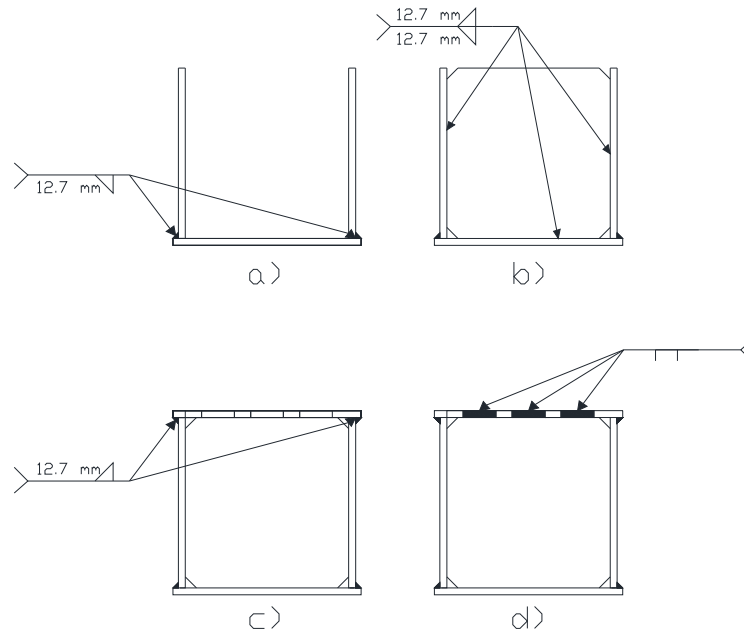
Secuencia para la colocación de diafragmas interiores en columnas cajón con soldadura de tapón.
